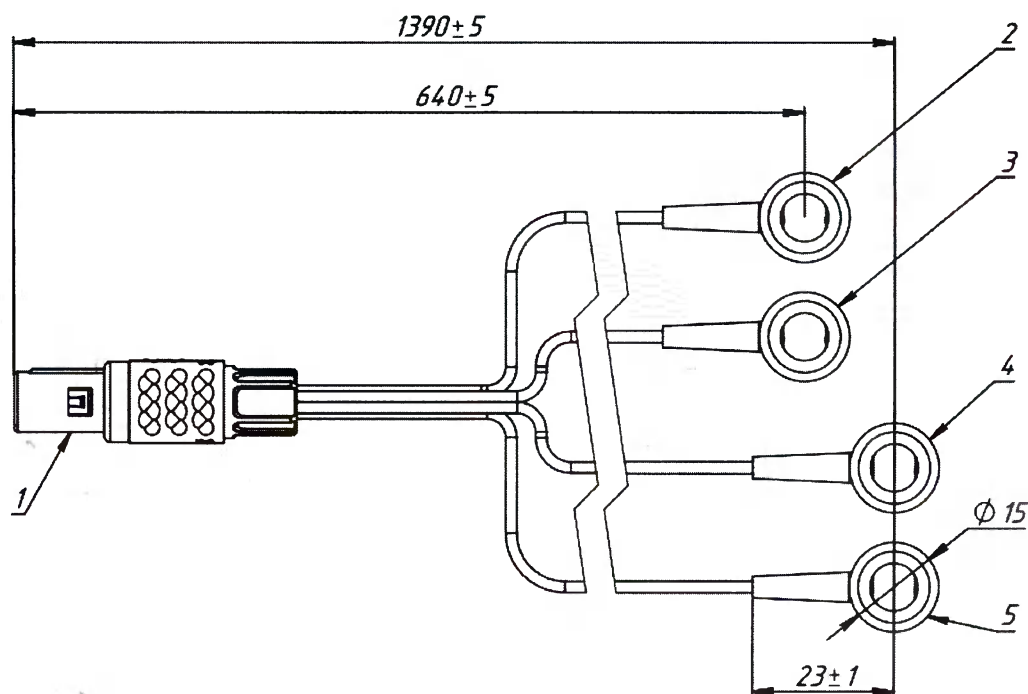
Внешний вид и габаритные размеры кабеля электродного Модуля базового
